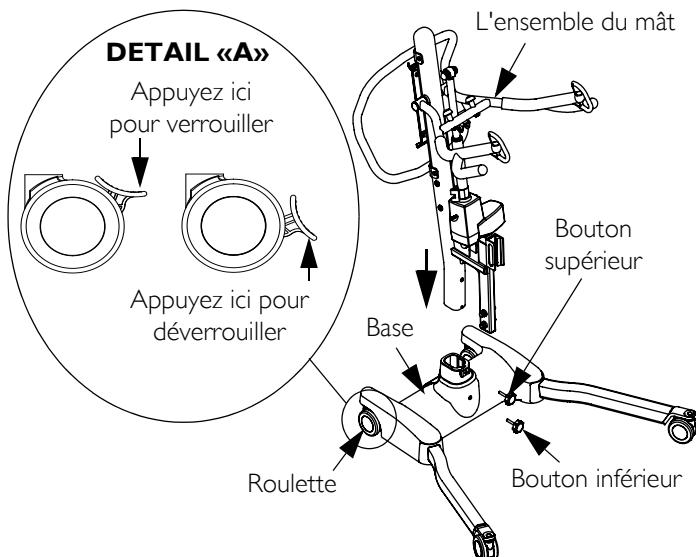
Assemblage de l'ensemble du mât à la base
